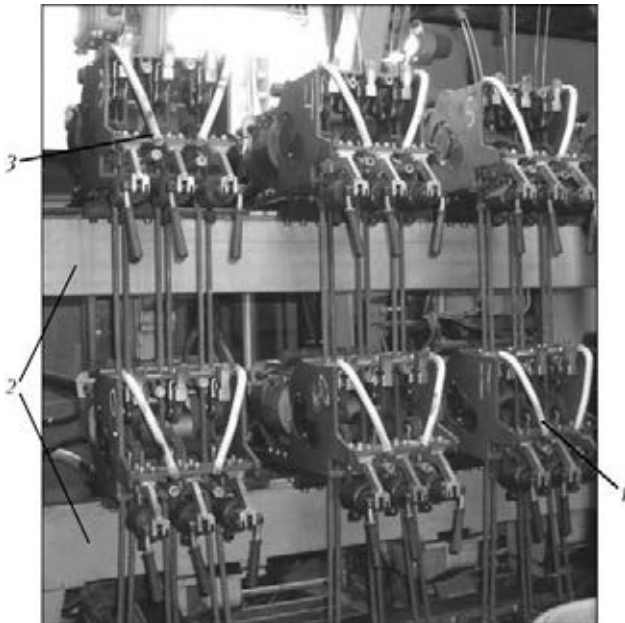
Внешний вид сварочных аппаратов АШ-110, собранных в блоки: 1, 3 — рабочие и дублирующие сварочные аппараты соответственно; 2 — траверсы для крепления аппаратов
